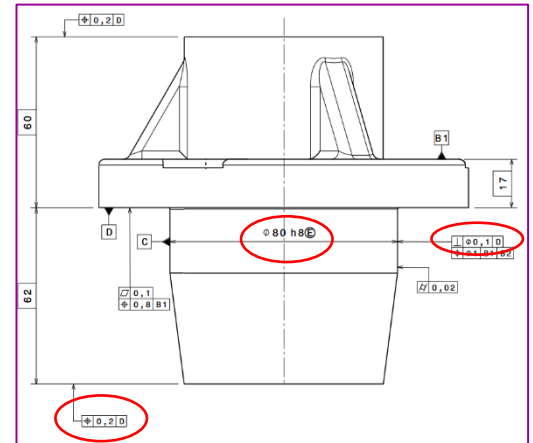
Section du plan de cotation du Pallier mélangeur.
